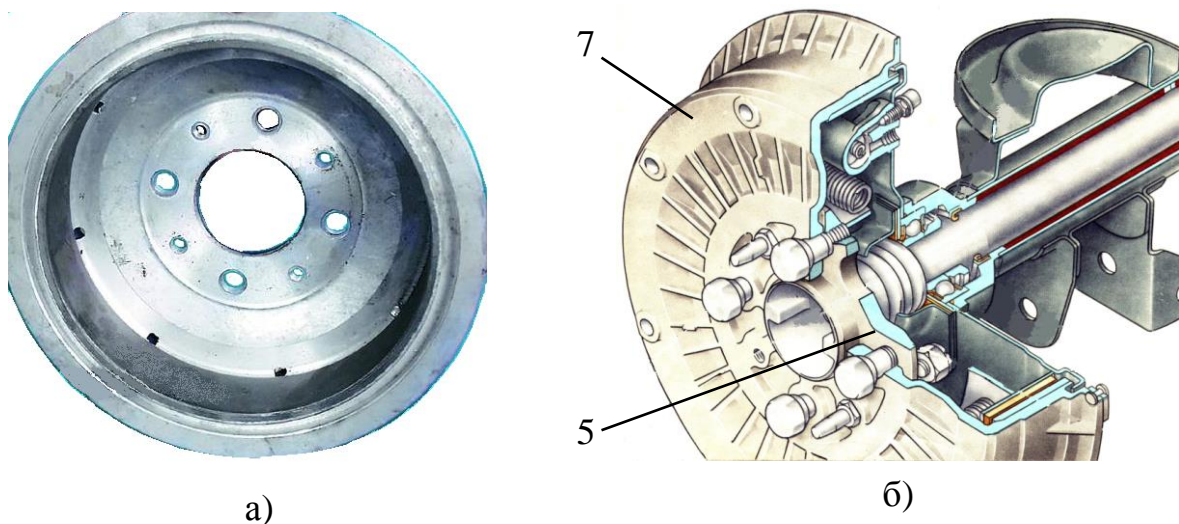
Конструкция барабанного тормозного механизма: а – тормозной барабан вид изнутри; б – тормозной механизма в сборе; обозначения позиций см. рис. 2.4
